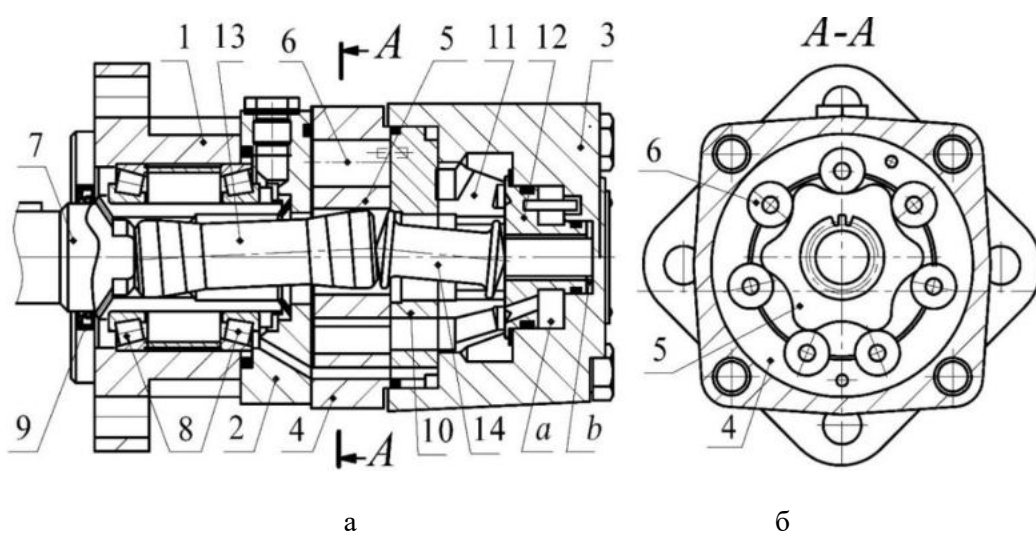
Героторный гидромотор: а – продольный; б – поперечный разрезы
